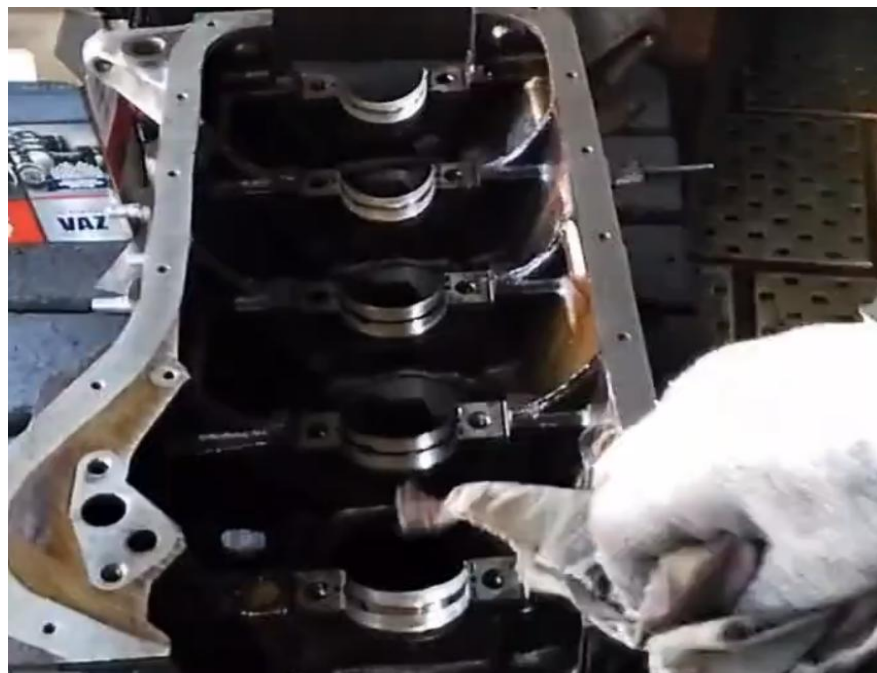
Подготовка блока цилиндров и рабочего места к работе
